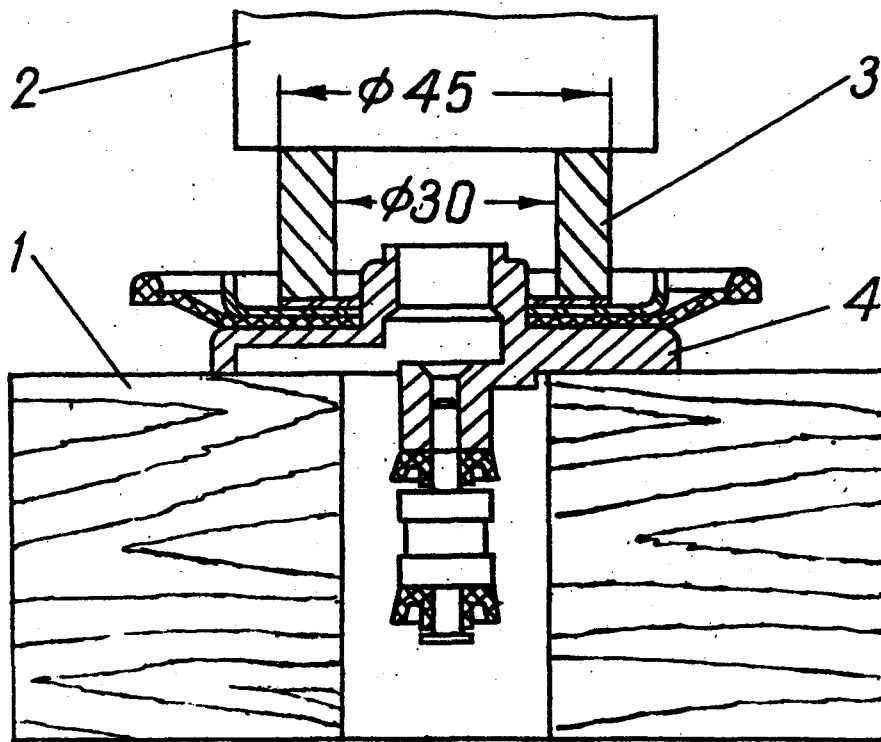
Напрессовка пластинчатой шайбы на клапан управления:
